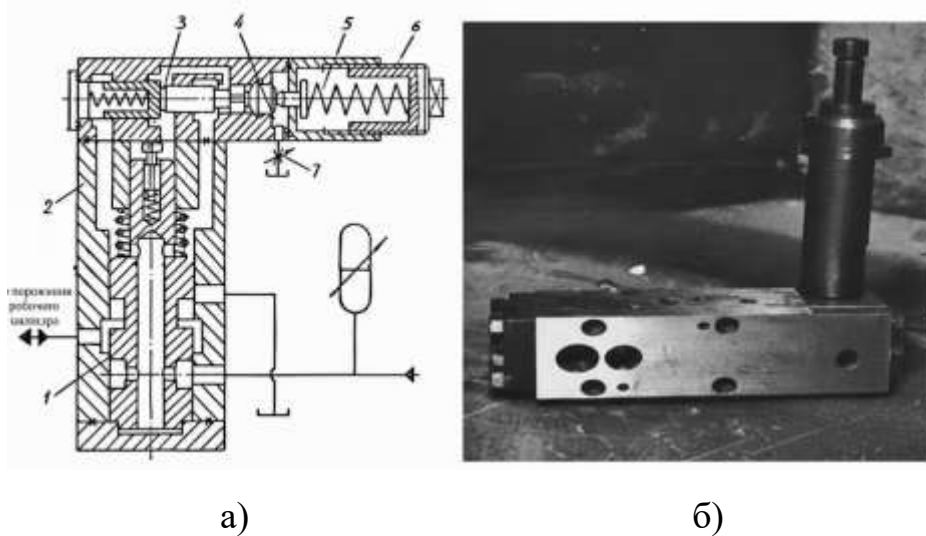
Віброзбуджувач типу А1Ш1-Б32: а) конструктивна схема; б) загальний вигляд: 1 – двокромковий золотник; 2 – кришка корпусу;
